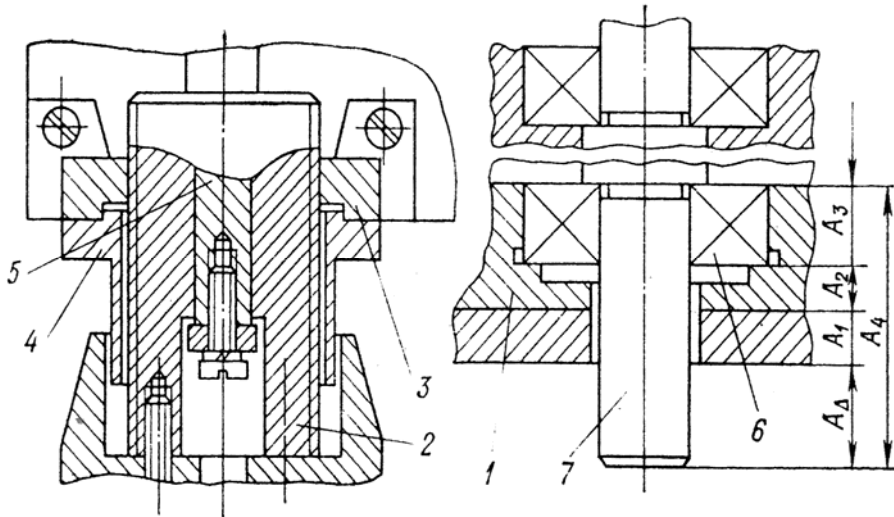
Узел подшипникового соединения: 1 – стакан; 2 – винт; 3- кронштейн;
